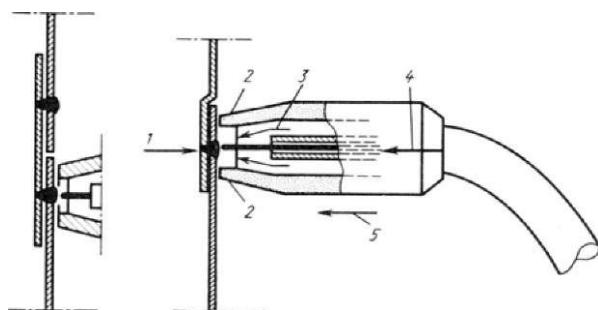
Точечная сварка тонких листов, один из которых выполнен с накладной лентой, а другой с отбортовкой: 1 - сварная точка; 2 - мундштук; 3 - защитный газ; 4 - размотка с выдержкой времени; 5 - небольшое усилие сжатия
